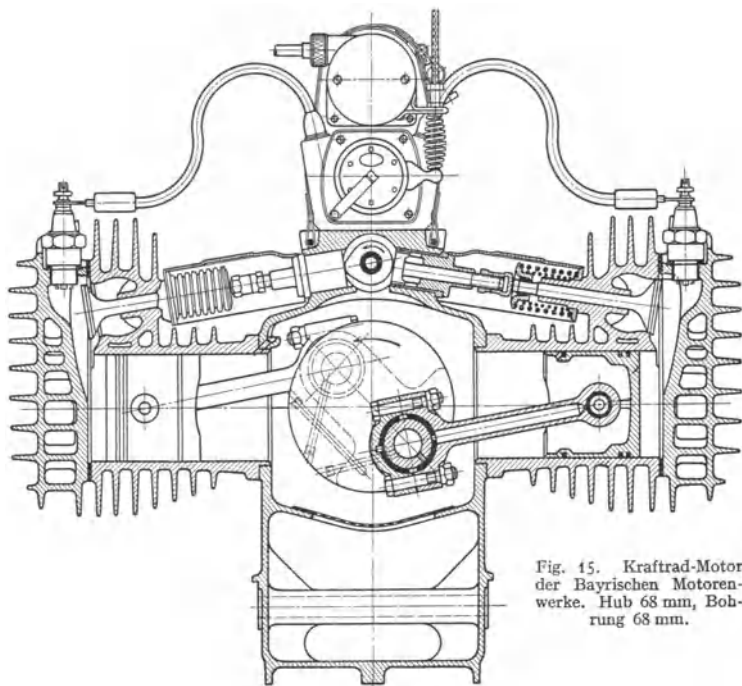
Kraftrad-Motor der Bayerischen Motorenwerke. Hub 68 mm, Bohrung 68 mm.
